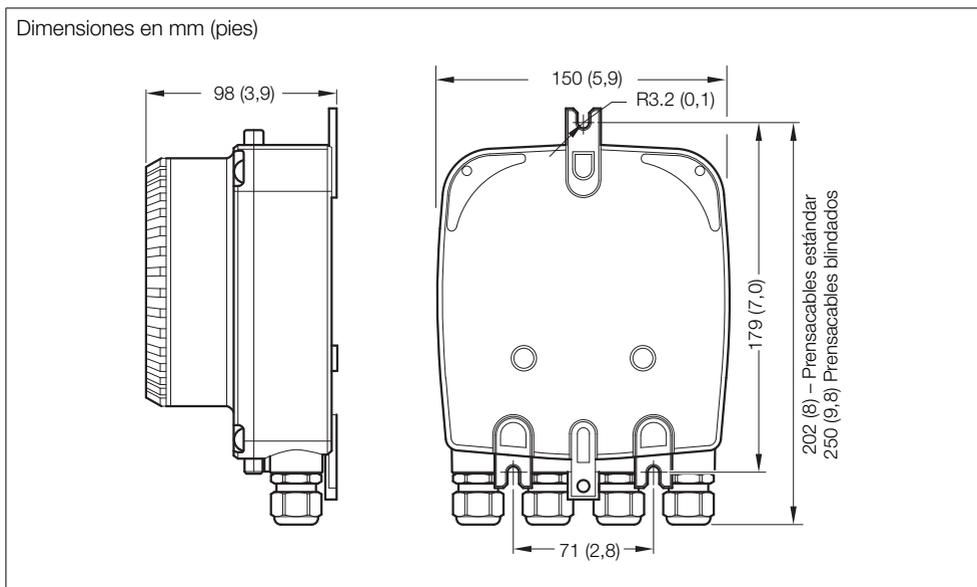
Dimensiones del transmisor remoto (se muestran prensacables estándar)
